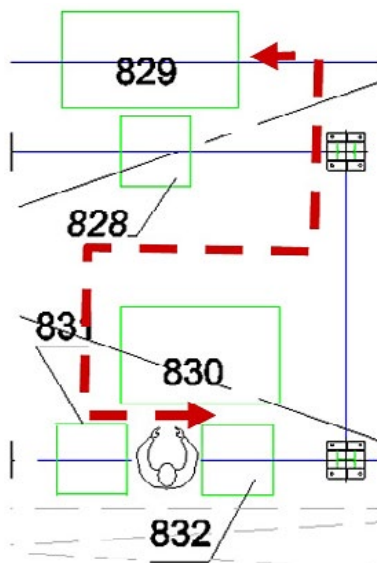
а. Было: сложная траектория перемещения сварщика с деталью из-за последовательного размещения сварочных машин 832 и 831
